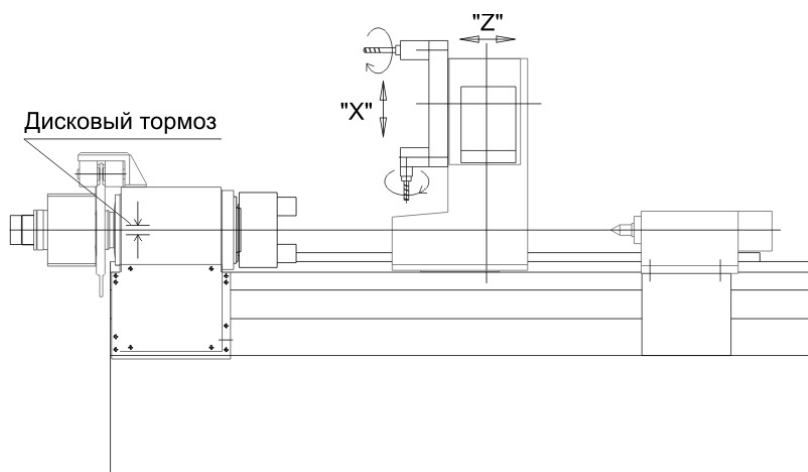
Центр токарный с устройством позиционирования шпинделя, револьверной головкой для токарного и приводного инструмента
